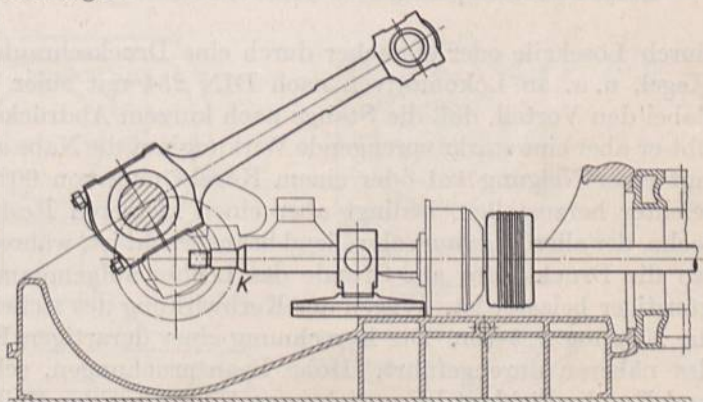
Einseitig geführter Gasmaschinenkreuzkopf, Maschinenfabrik Augsburg-Nürnberg, so ausgebildet, daß der Kolben nach vorn zu ausgebaut werden kann.
